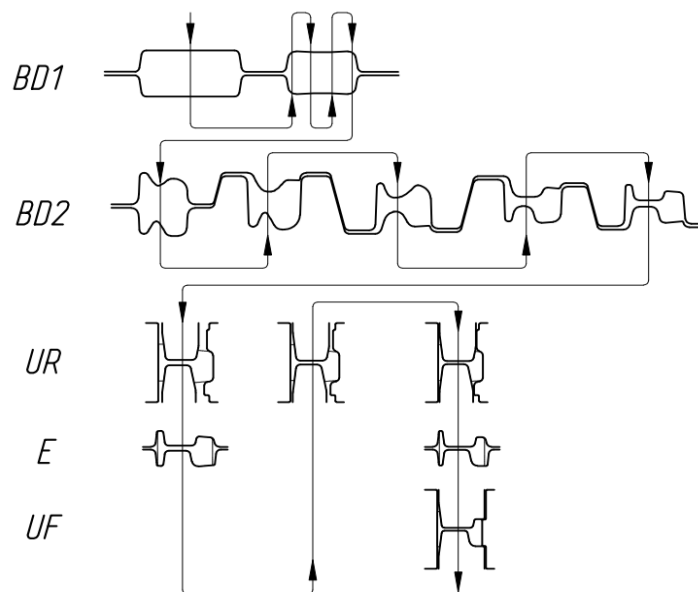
Схема прокатки заготовки трамвайных рельсов Т62
